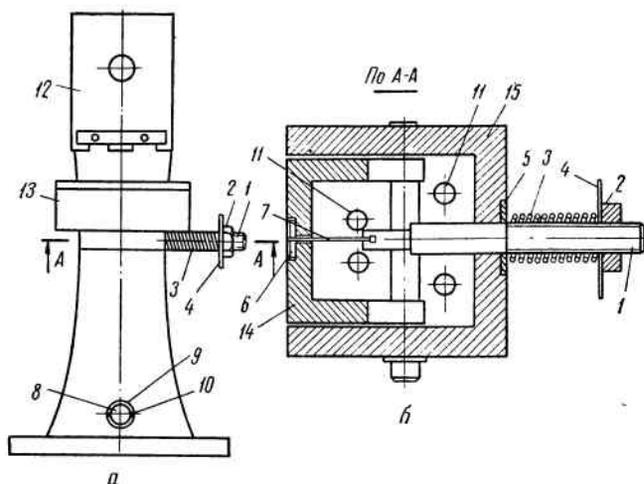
Общий вид (а) и разрез (б) приспособления:
